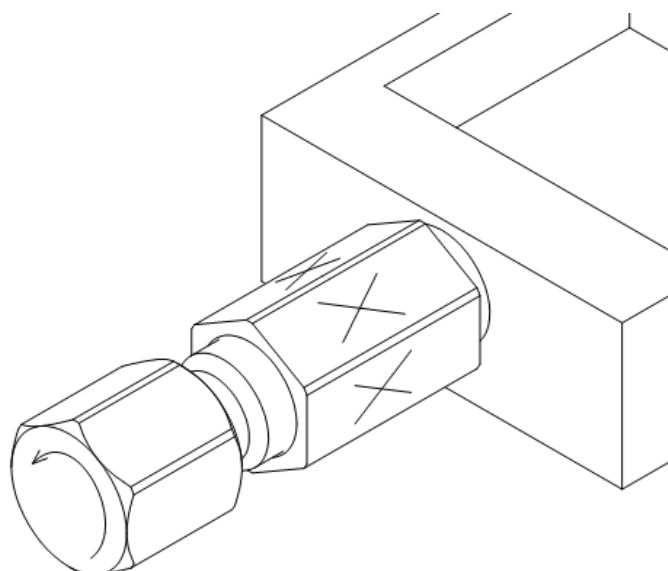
Откручивание приспособления 7290-0214.00.000.00-02
